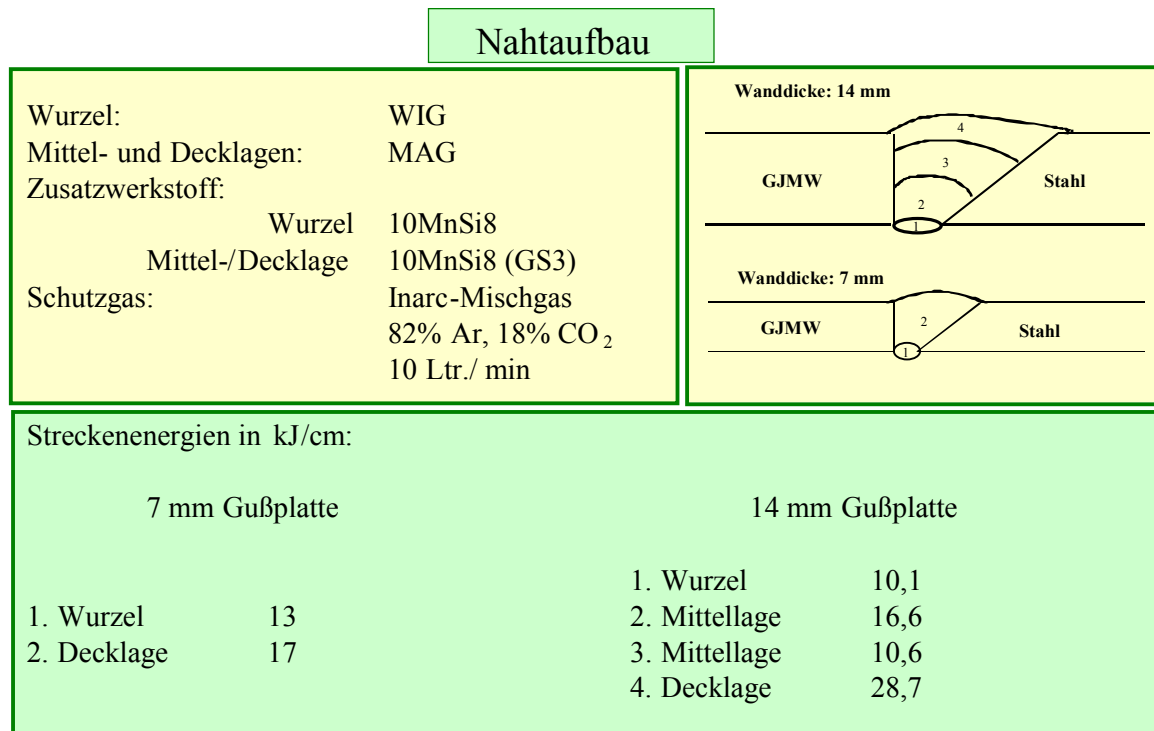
Schweißtechnologie der Verbundschweißung
